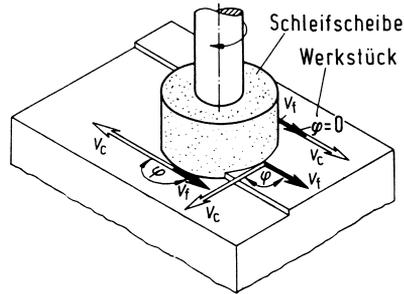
Vorschubrichtungswinkel φ beim Schleifen mit Stirnfräser (nach DIN 6580)
